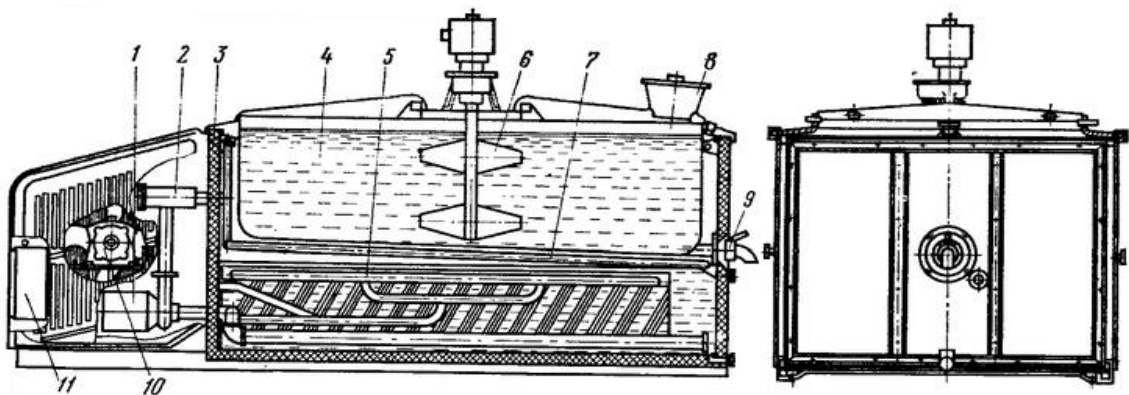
Танк-охолоджувач молока ТОМ-2А: 1 – насос; 2 – фільтр; 3 – корпус; 4 – ванна; 5 – випарник; 6 – мішалка; 7 – система зрошування; 8 – молочний фільтр; 9 – зливний патрубок; 10 - компресорно-конденсаторний агрегат; 11 – шафа управління
